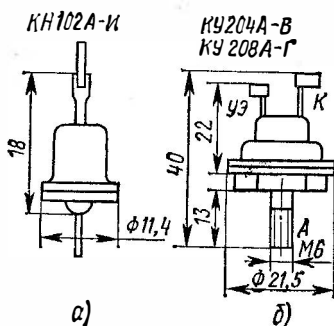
Общий вид и габаритные размеры динисторов (а, б)
